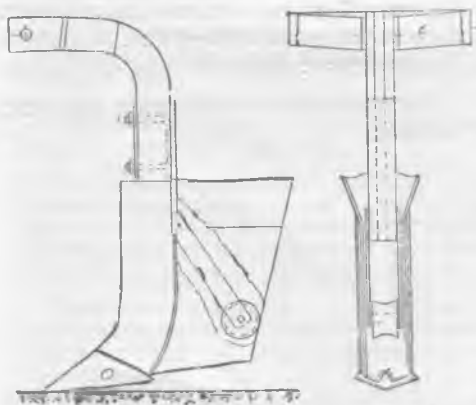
Положение приспособления в сошнике лесопосадочной машины и способ его крепления.
